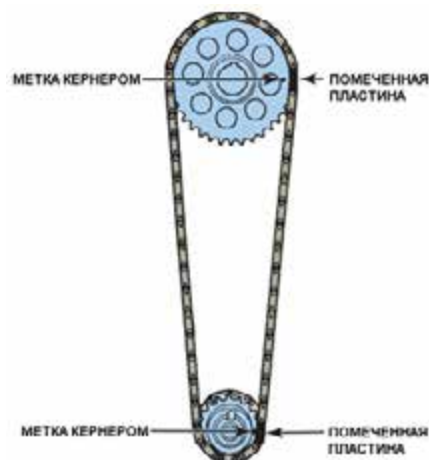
Некоторые цепные приводы газораспределительного механизма имеют метки на планках цепи, которые следует совместить с соответствующими помеченными зубьями звездочек коленчатого вала и звездочки привода распределительного вала; источник: *Pearson Education, Inc.
